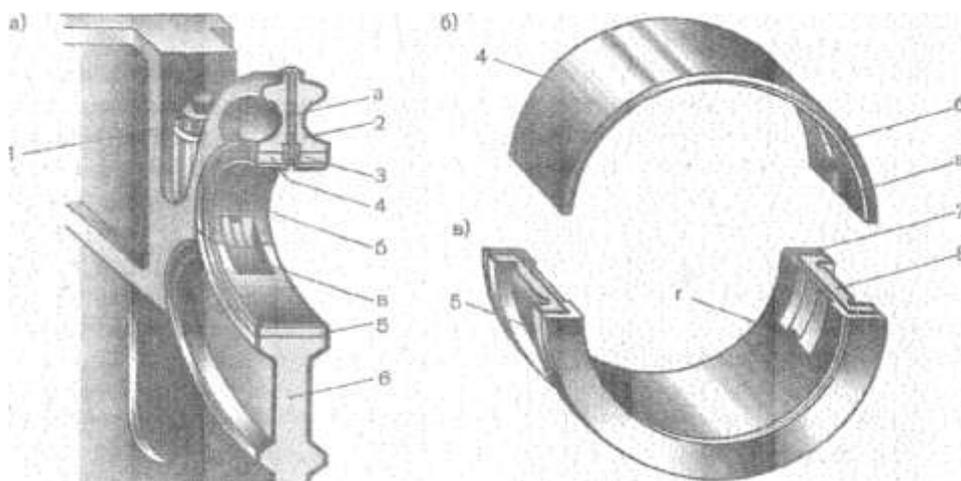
Коренной подшипник дизеля 6ЧРН32/48
